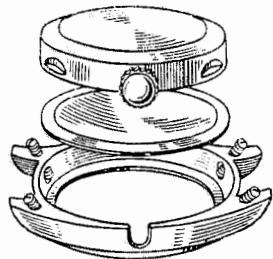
Влагозащитный корпус защелкивающегося типа.
